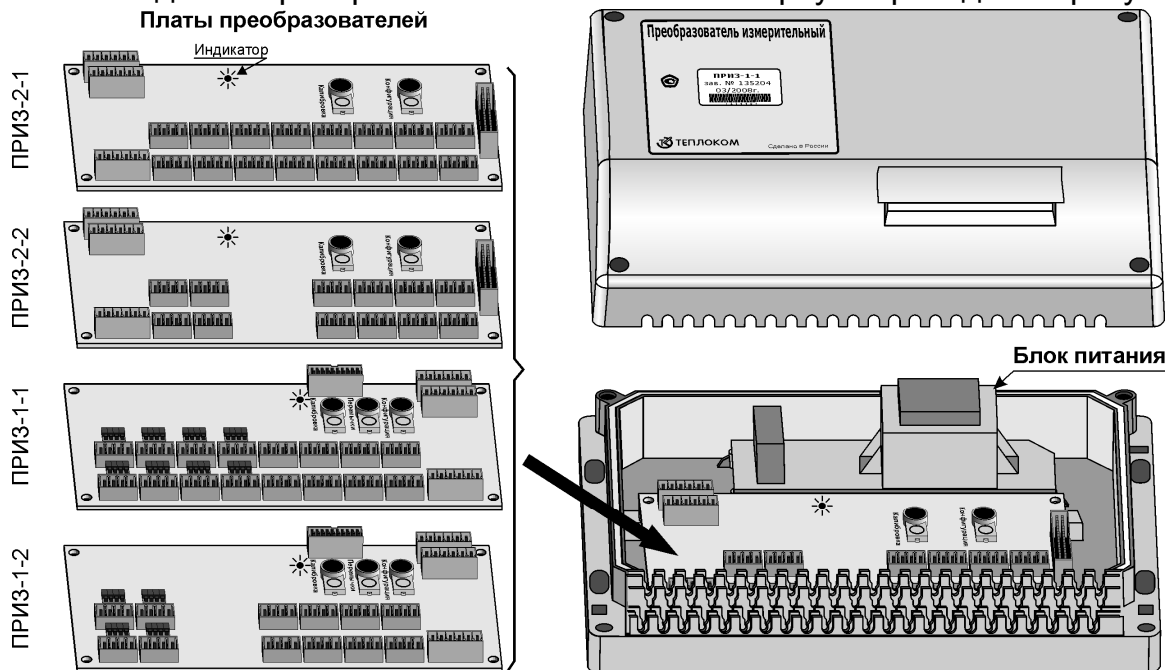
Внешний вид плат преобразователей и частей корпуса
